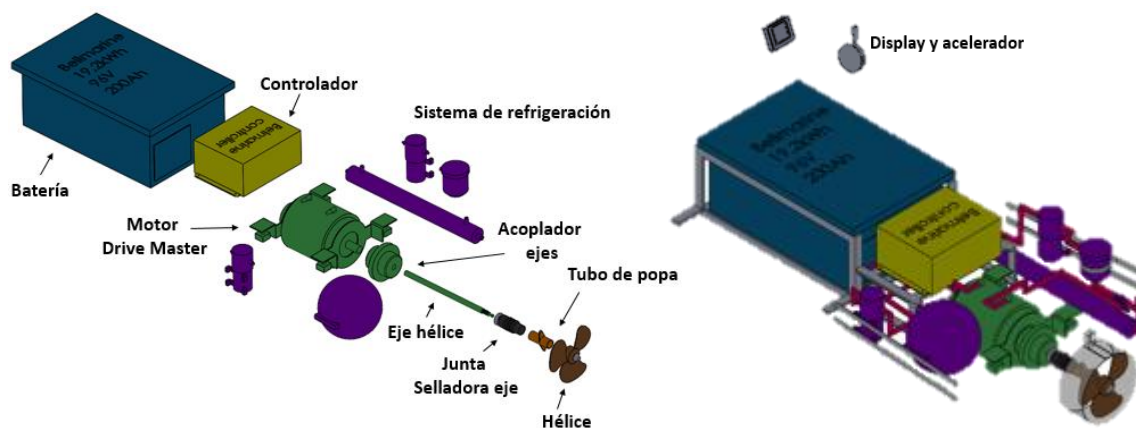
Vista explosionada y conjunto en layout de los elementos del sistema de impulsión del diseño final (Fuente: elaboración propia).
